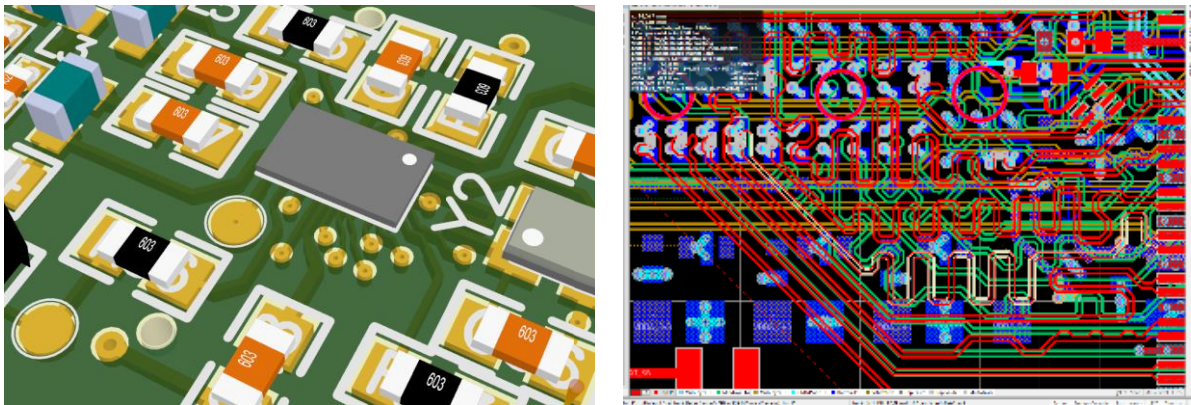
Ausschnitt aus dem PCB-Design eines komplexen Sensors
